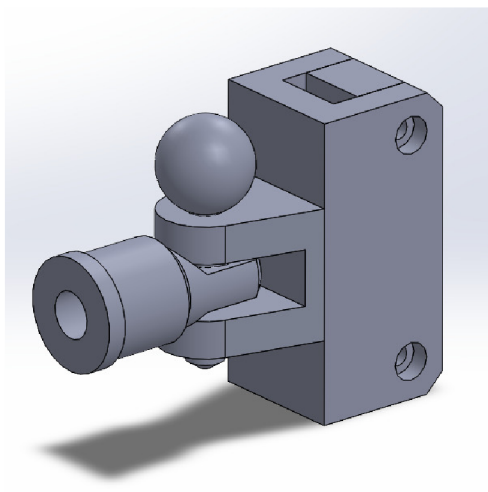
Тривимірний модель вузла захвату ручки двері
